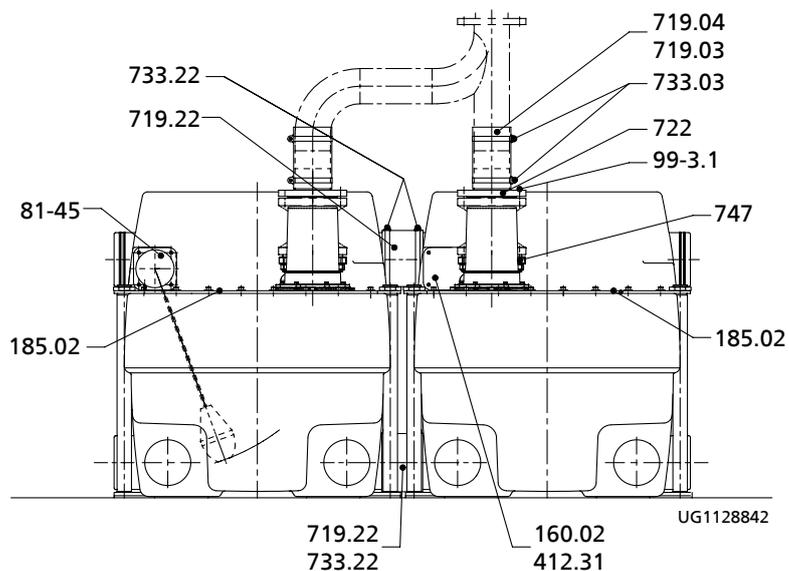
Сборочный чертеж Compacta UZ900 с 2 резервуарами
